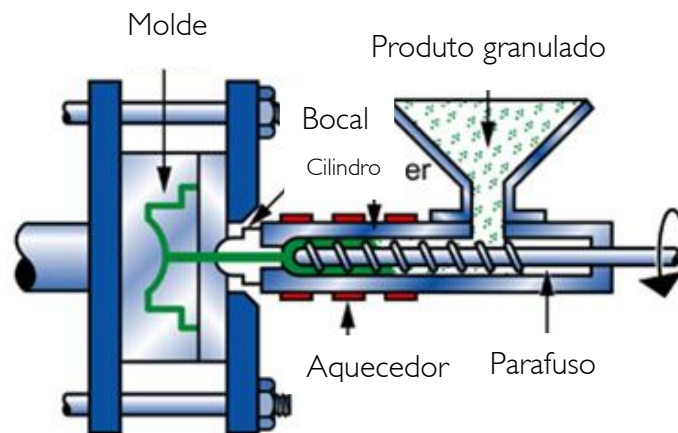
Processo de moldagem por injeção (Fonte: CES EduPack 2017)
